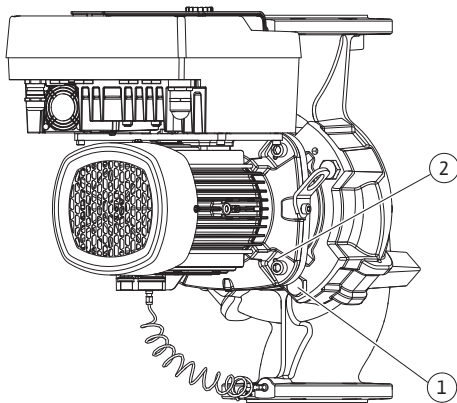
Abdrücken des Einstecksatzes über Gewindebohrungen (je nach Pumpentyp)
